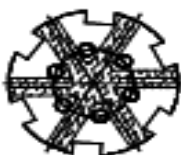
Фрезер забойный типа ФЗ легкого вида
